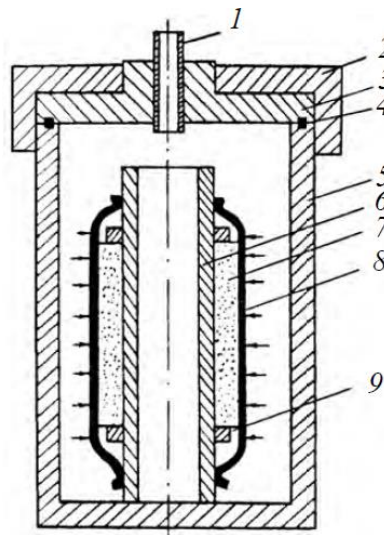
Схема гидростатического прессования втулок: 1 – труба высокого давления; 2 – крышка камеры; 3 – затвор; 4 – уплотнительная прокладка; 5 – корпус камеры прессования; 6 – сердечник; 7 – порошок; 8 – эластичная оболочка; 9 – фиксатор сердечника
